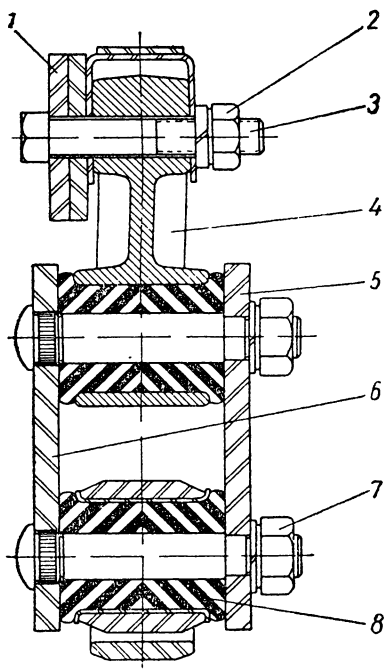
Крепление переднего конца задней рессоры автомобиля М-72:
